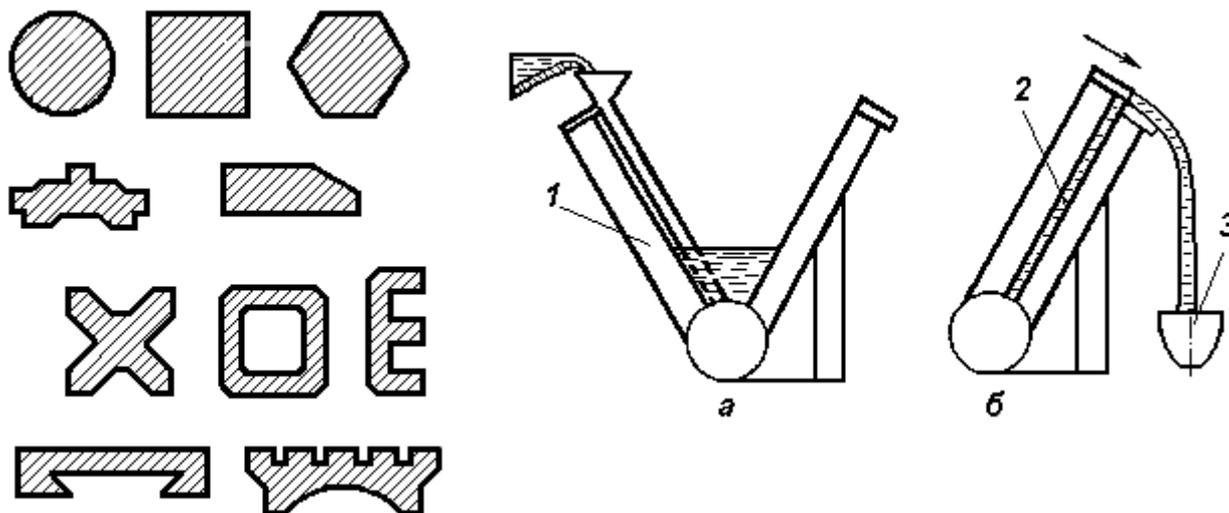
Образцы отливок, полученных непрерывным литьём
